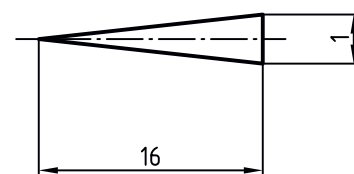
Konizität des Aussengewindes 1:16. Das Gewindeprofil ist rechtwinkelig zur Rohrachse.
